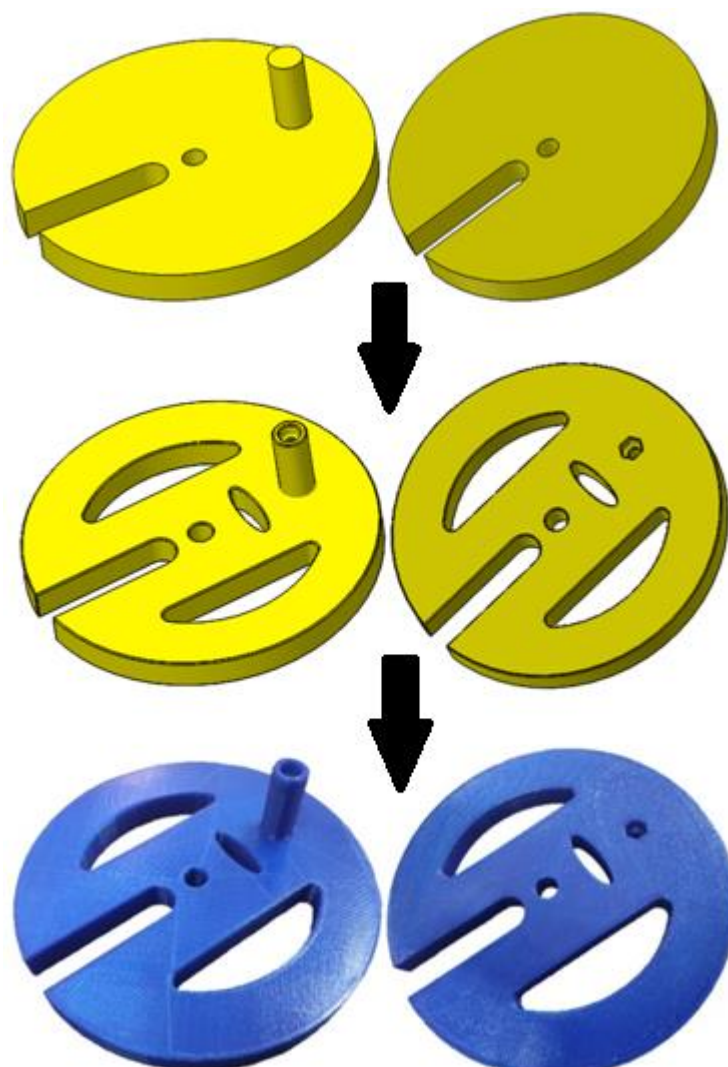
De arriba a abajo: pieza inicialmente diseñada, pieza diseñada para la impresión 3D, pieza real impresa
